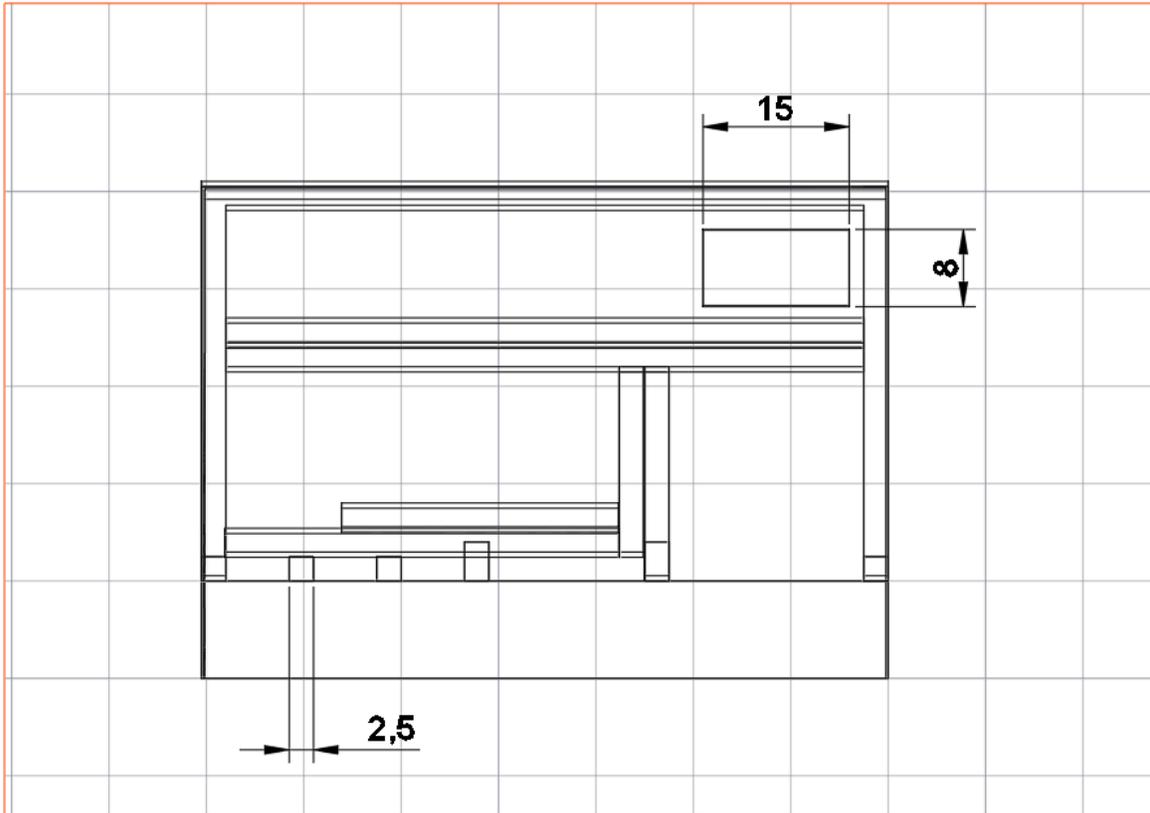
Dimensiones de módulo de entrenamiento, vista frontal.
